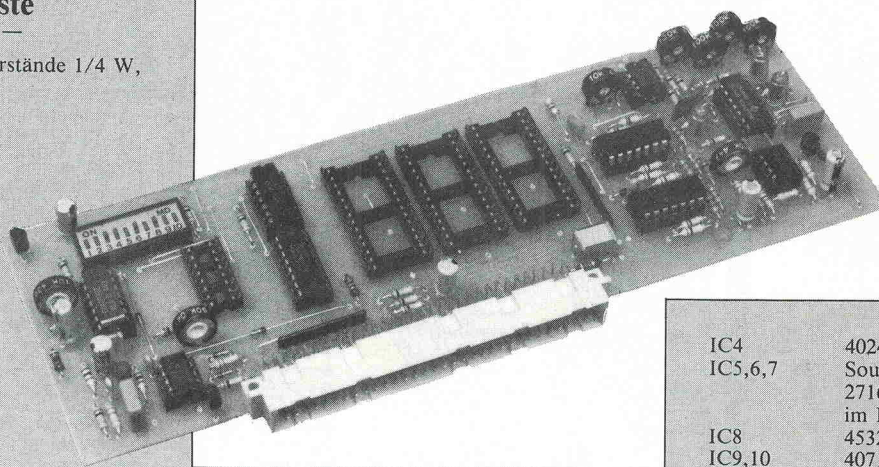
Die fertig bestückte Voice-Platine. Acht Trimmer sind später abzugleichen.
